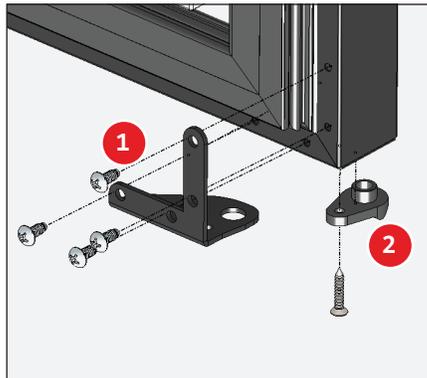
Componentes del conjunto de la bisagra inferior.
